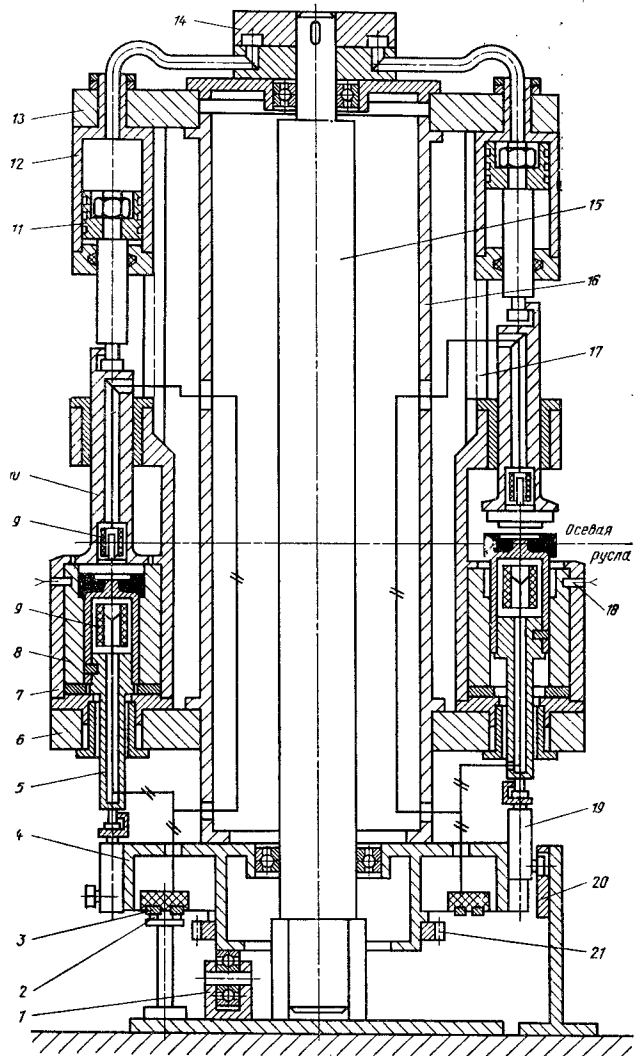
Схематический чертеж ротора с гидромеханическим приводом основных рабочих органов для полугорячей штамповки:
